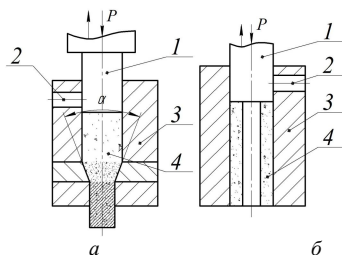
Схемы мундштучного прессования: а – для получения прутков; б – для получения трубчатой заготовки: 1 – пуансон; 2 – окно подачи порошкового материала; 3 – матрица; 4 – навеска порошка
